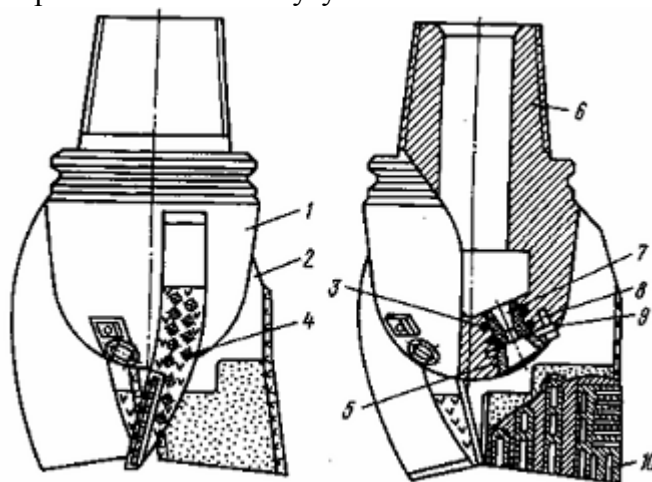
Трехлопастное долото типов М(а) и МС(б): 1 корпус; 2 – лопасти; 3 – уплотнительные кольца; 4 – твердосплавные штыри; 5- байонетная шайба; 6 - присоединительная резьба; 7 – сопло; 8 – болт; 9 – стопорная шайба; 10 – пластины.
